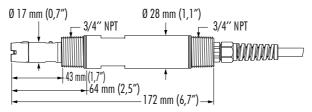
HI7640-58ZZ OD óptica con cable acoplado
